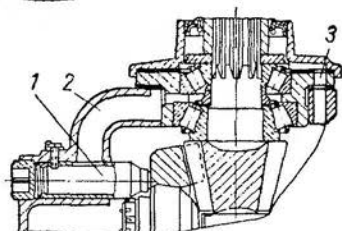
Главная передача автомобиля ГАЗ-53А:
